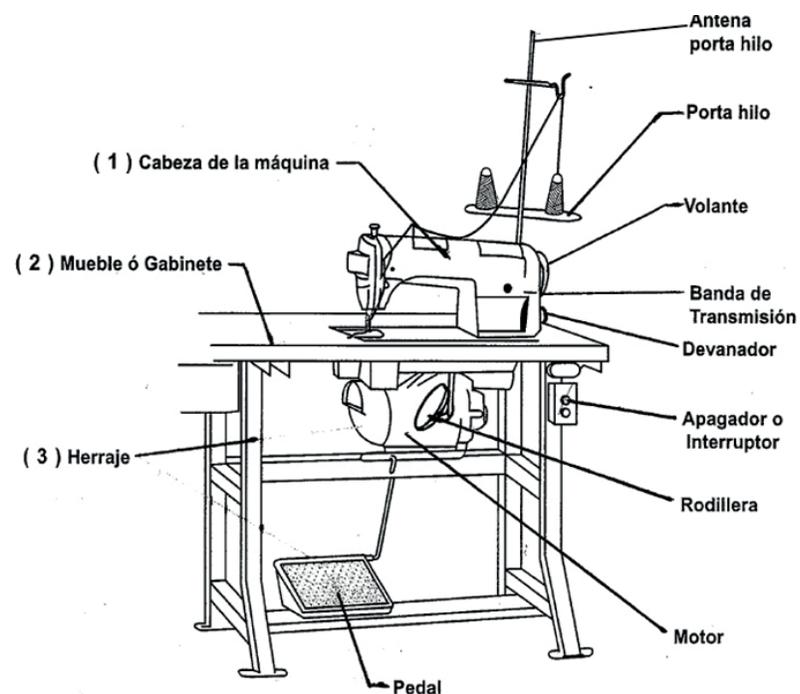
Partes de la maquina industrial recta. Fuente: Serrano, C. (2005).
